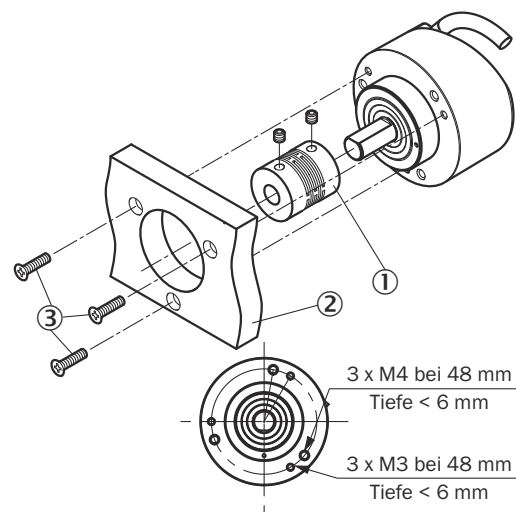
Anbau Klemmflansch über flanschseitige Gewindebohrungen
